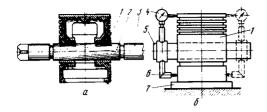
Инструмент и приспособление для ремонта отверстий в бобышках поршня:
